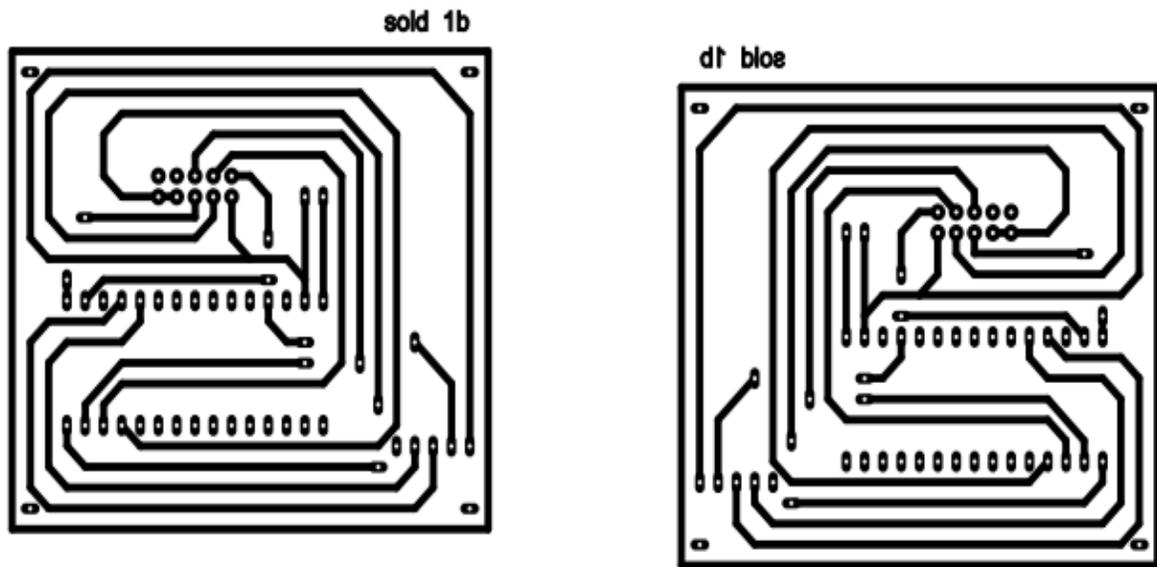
Diseño del circuito electrónico de la PCB para uso interno del control remoto
